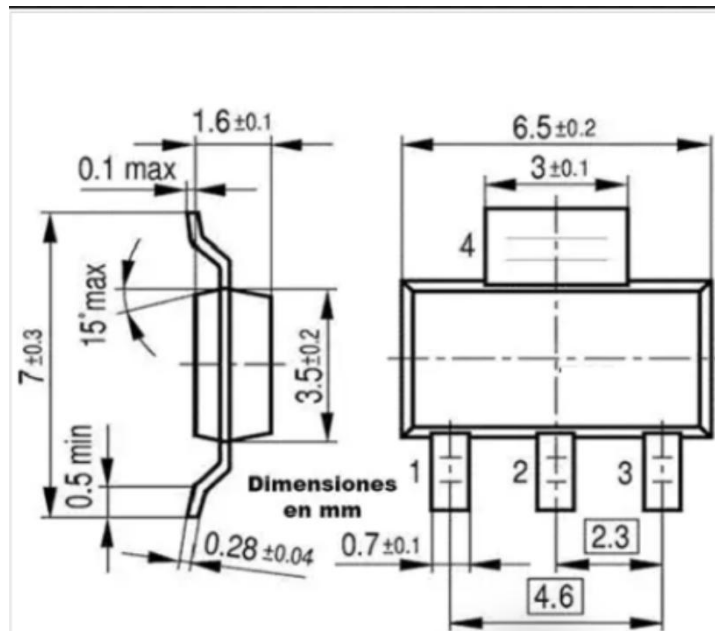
Габаритні розміри мікросхеми LM1117MPX-3.3
